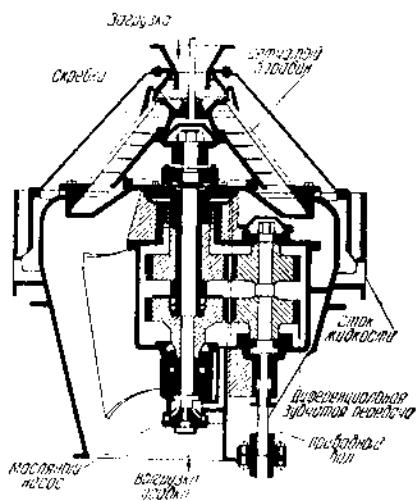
Центрифуга Эльмора новейшей конструкции.
